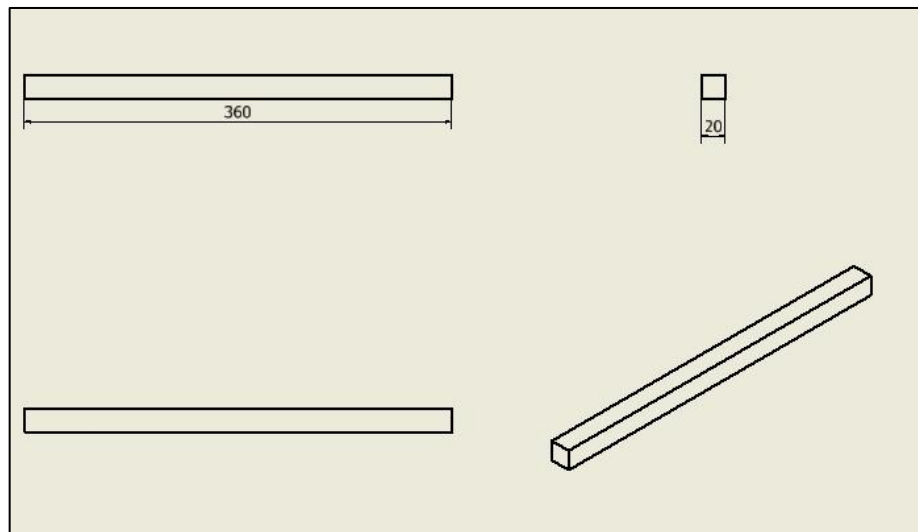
e 12 – Fuso e Guia Suporte Spindle.
